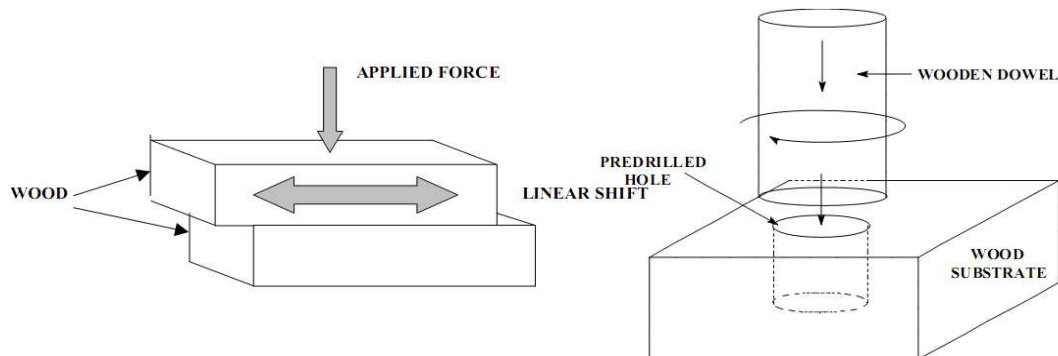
Soudage du bois par soudage linéaire (à gauche) et soudage rotatif (à droite)
